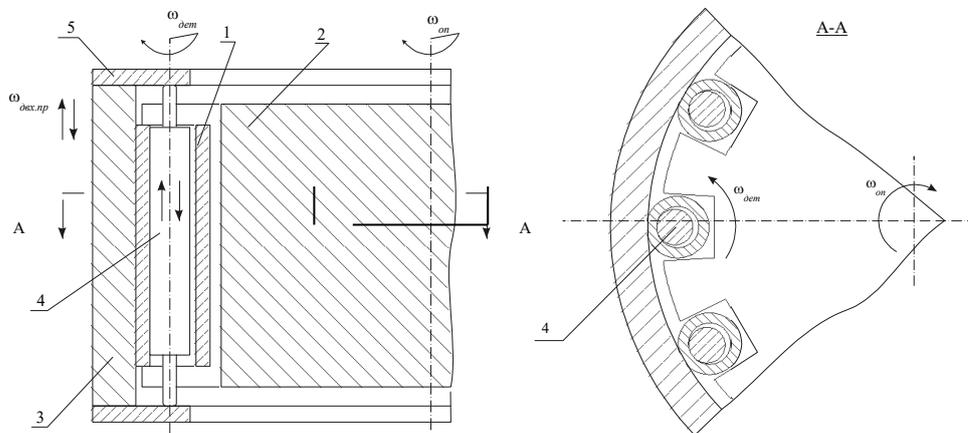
Схема одновременной обработки наружной и внутренней поверхности втулки
